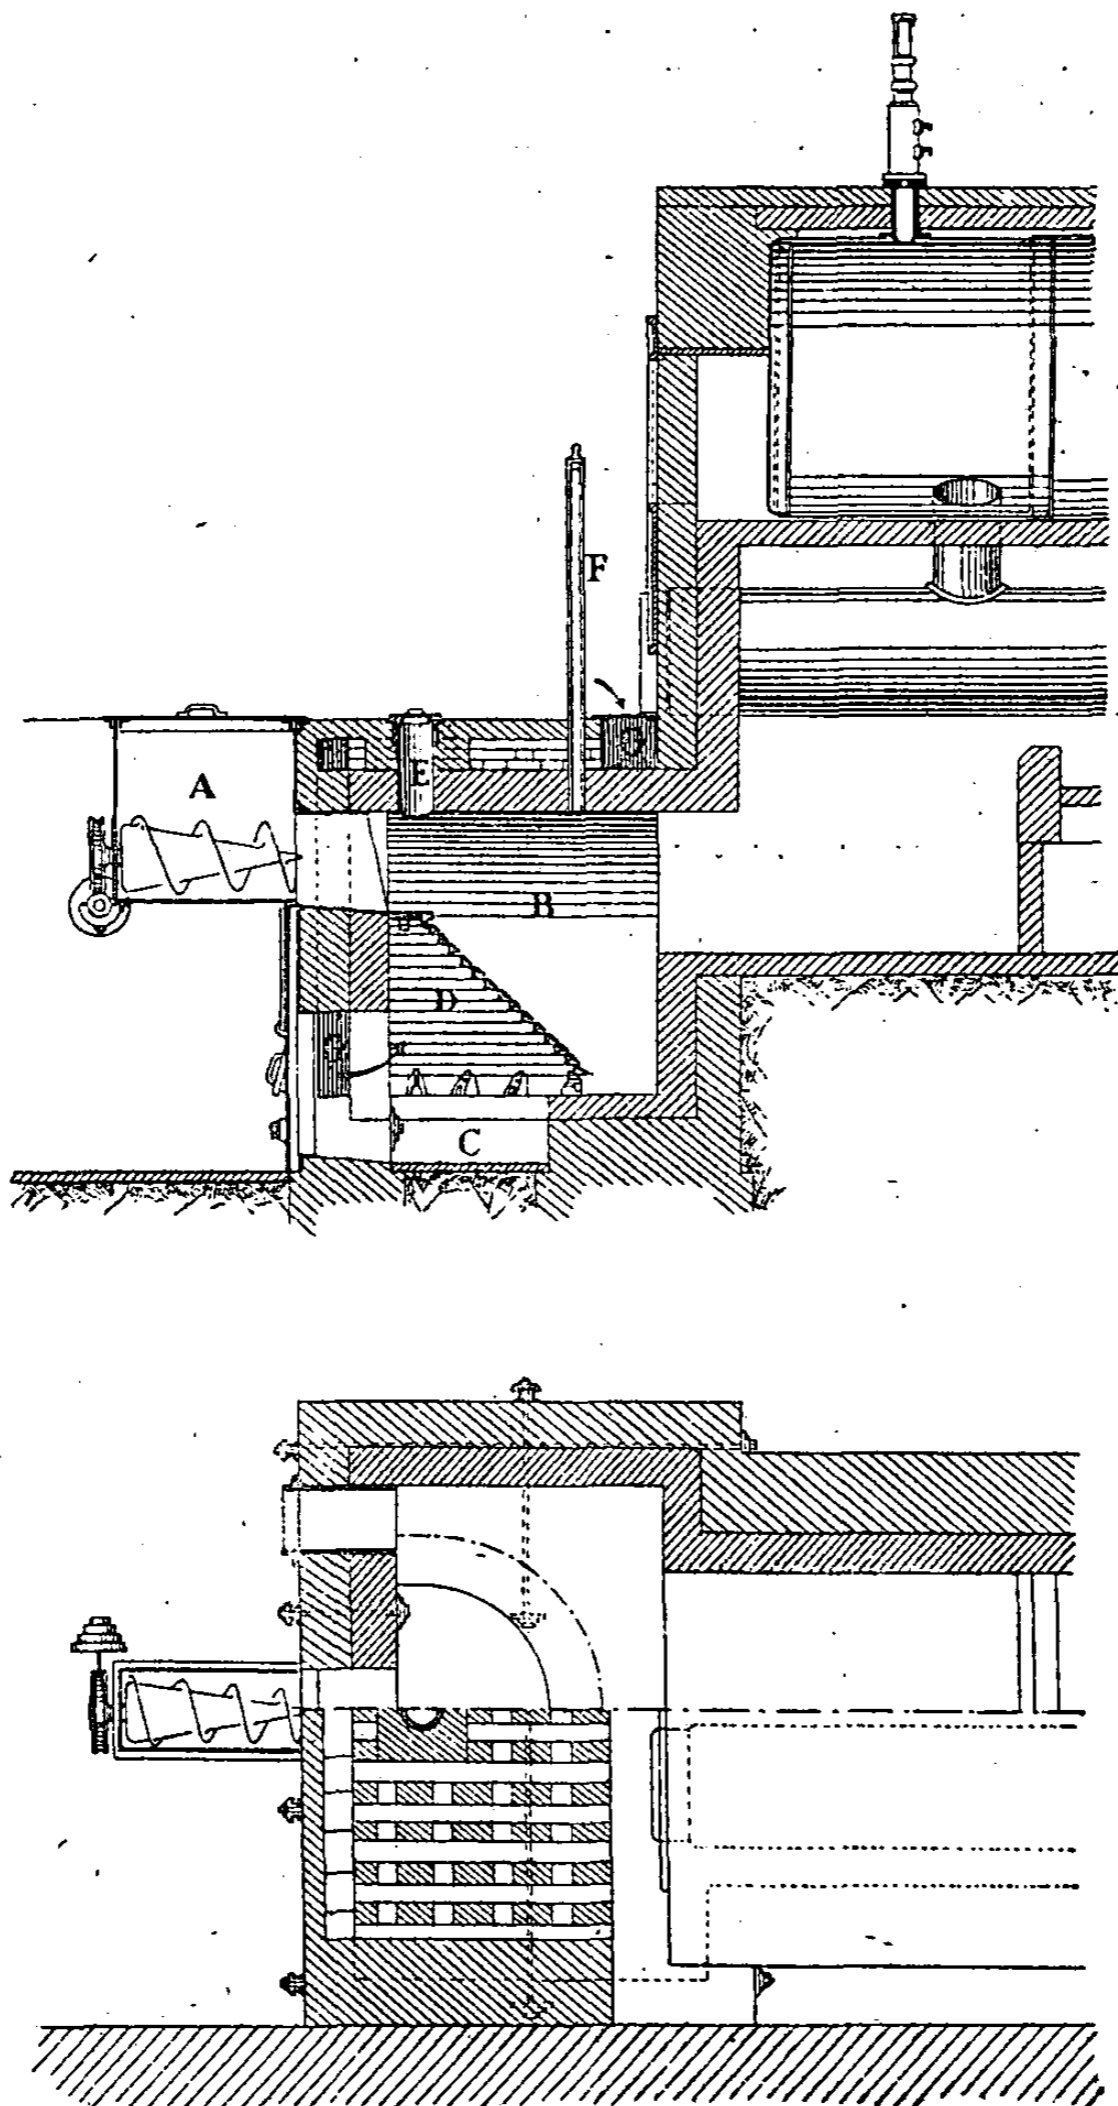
et 363. — Coupe et plan du foyer Godillot.
